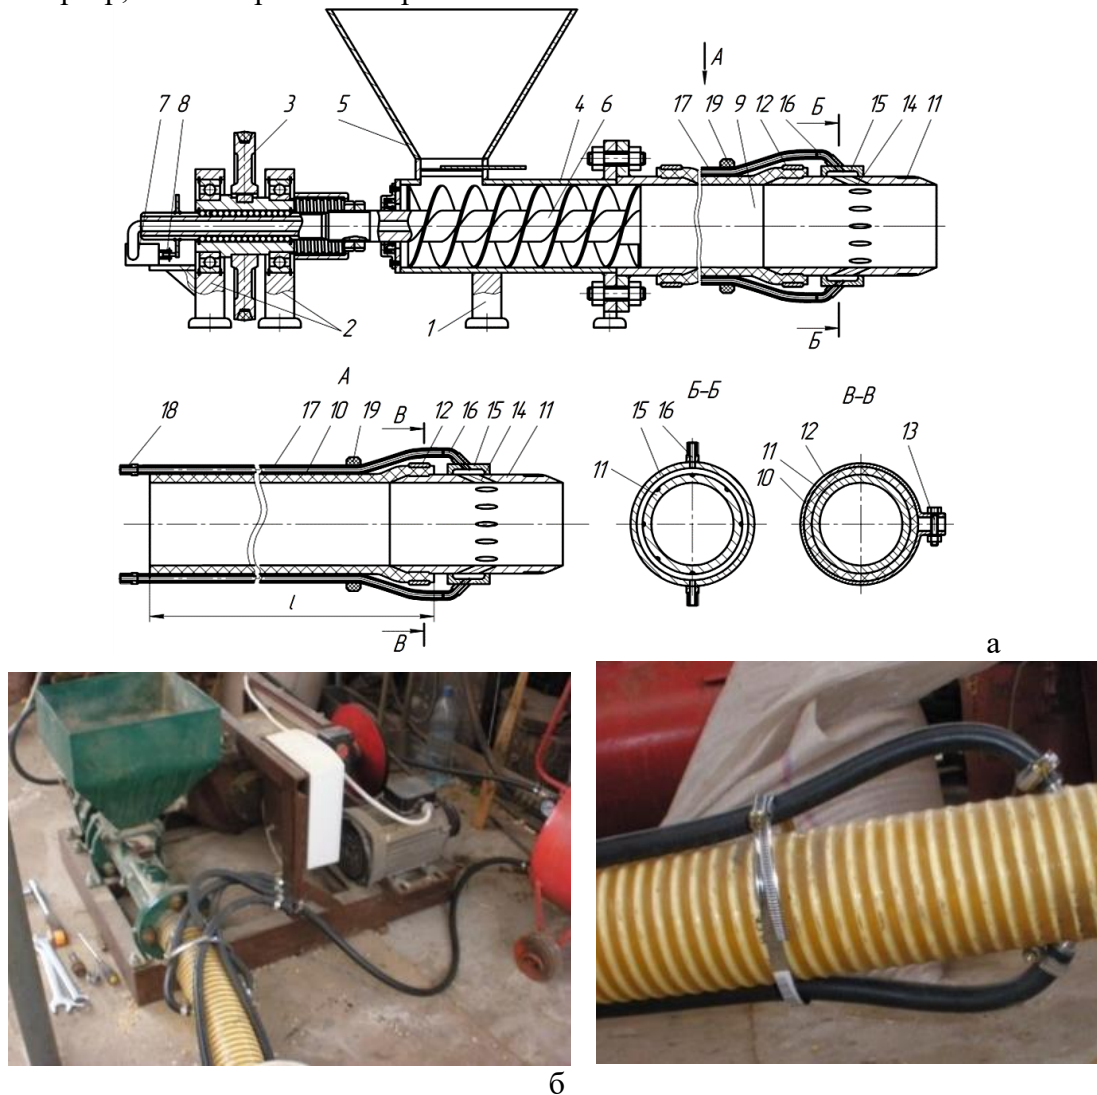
Конструктивна схема (а) та загальний вигляд (б) пневмо-шнекового транспортера з під'єднаними шлангами живлення до гнучкого кожуха
